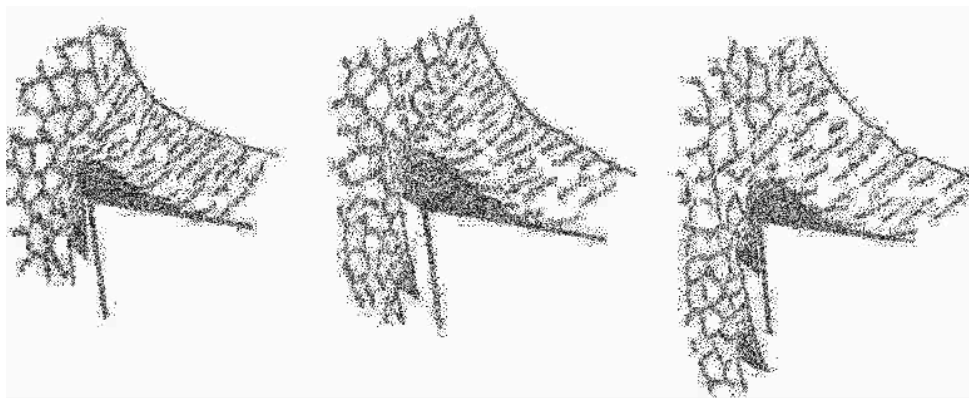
Схема образования шероховатости поверхности вследствие срывов нароста
